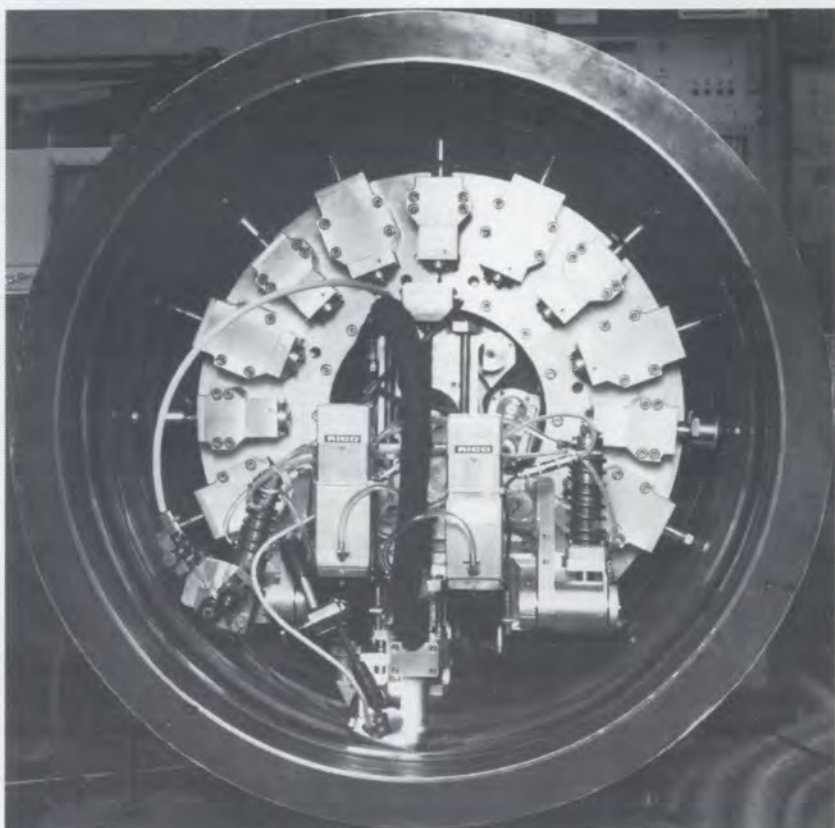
Сварочная машина для внутреннего плакирования трубопроводов
